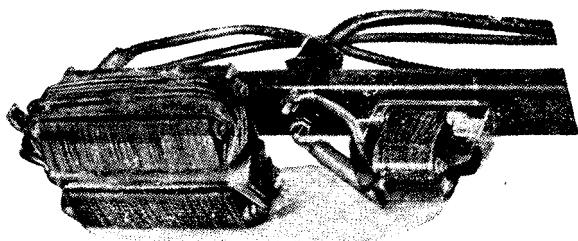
Опытный образец приспособления с двумя электромагнитами.
